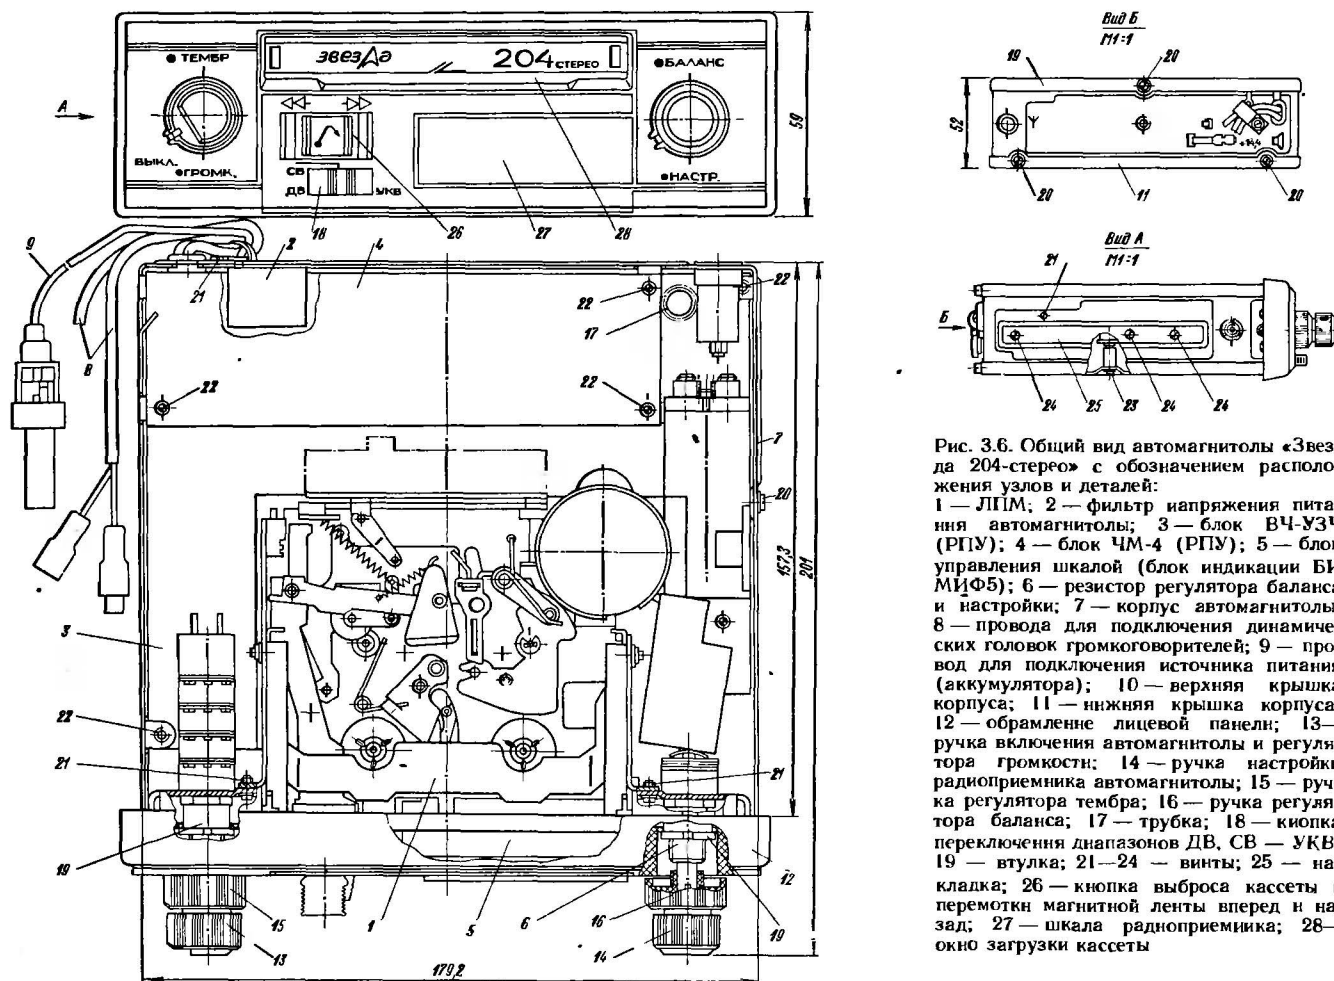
Общий вид автомагнитолы «Звезда 204-стерео» с обозначением расположения узлов и деталей:
